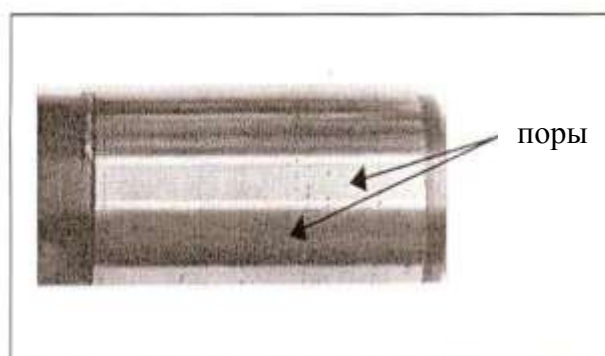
Вид чугунного образца после лазерной наплавки на предварительно оплавленную поверхность
